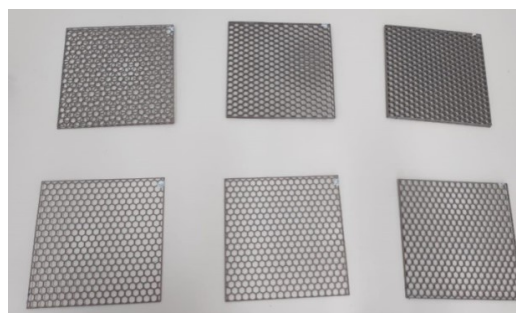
Algumas das estruturas empregadas no ensaio de dilatação.
